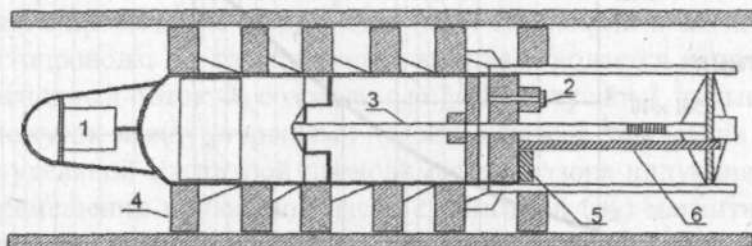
Схема герметизатора и расположение ИПШ: 1 - радиомаячок; 2 - мембрана; 3 - шток; 4 - уплотнители; 5 - радиопередающий блок; 6 - измеритель перемещения штока
